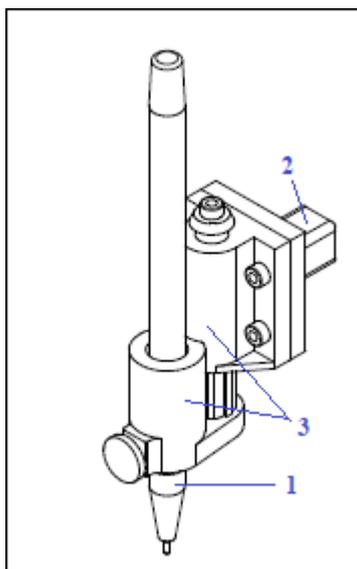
Модуль захвата пишущих инструментов, где 1 – пишущий инструмент; 2 – держатель захвата пишущих инструментов; 3 – захват пишущих инструментов
